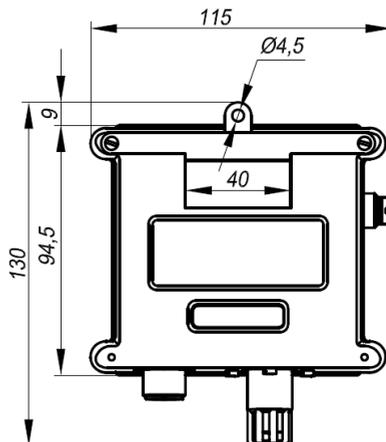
Присоединительные размеры датчика в пластиковом корпусе
